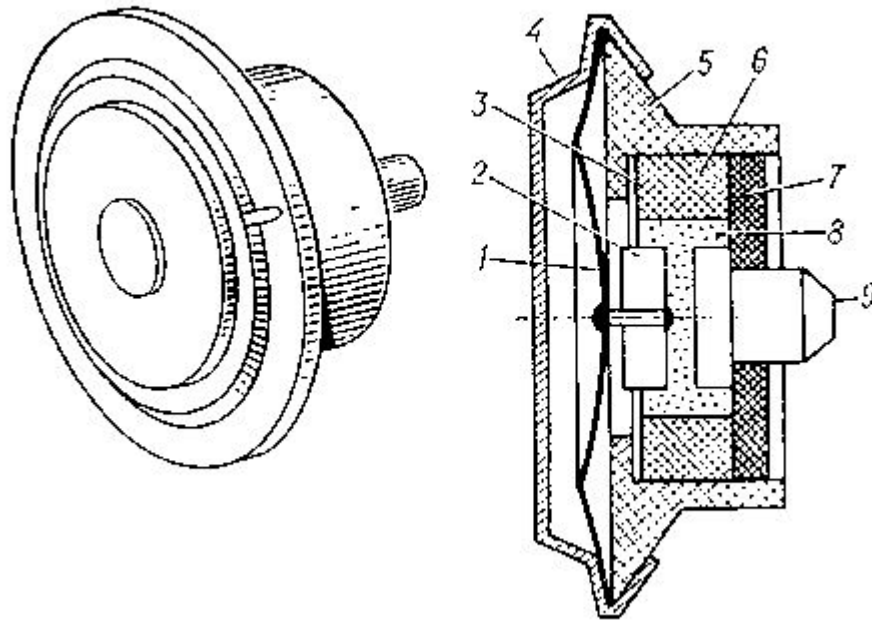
Капсюль типа МК-10 угольного микрофона: а — внешний вид; б — схема устройства; 1 — мембрана; 2 — подвижный электрод; 3 — слюдяная шайба; 4 — перфорированная металлическая крышка; 5 — корпус; 6 — пластмассовое кольцо; 7 — шайба; 8 — угольный порошок; 9 — неподвижный электрод.
